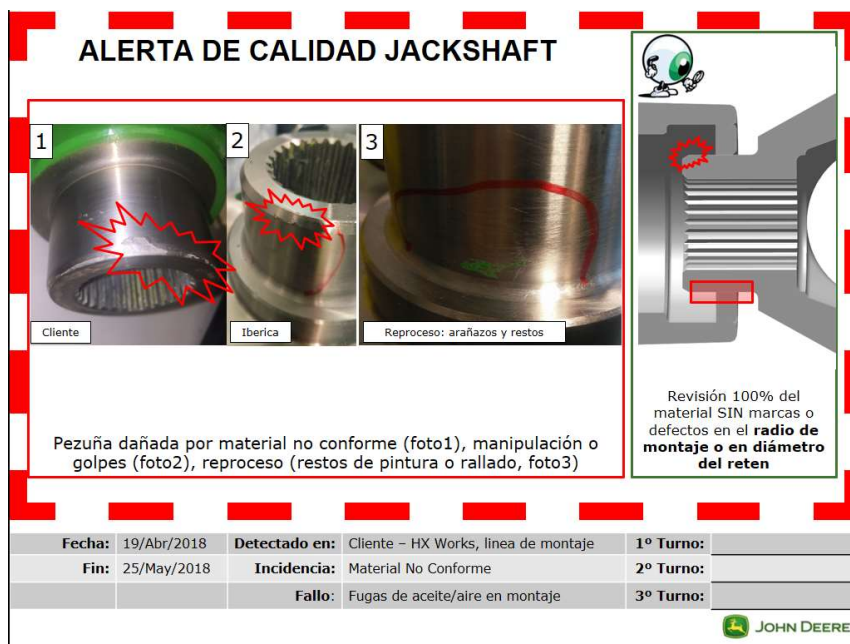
Alerta de calidad en caja de transmisión Jackshaft John Deere.
